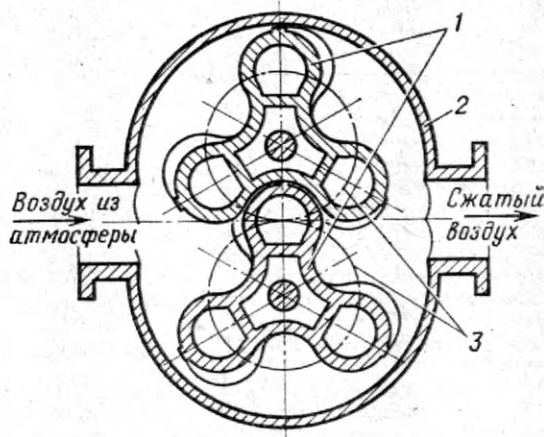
Схема роторного компрессора: 1 — роторы; 2 — корпус; 3 — шестерни
